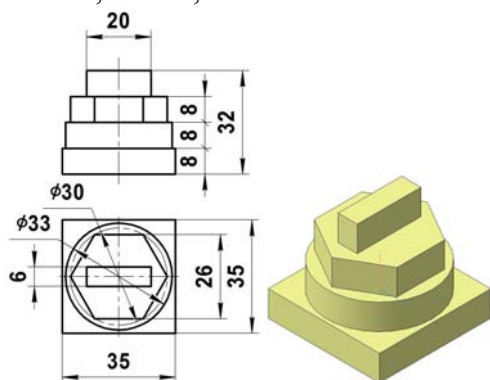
Зразок з охоплюваними валами характерної форми
